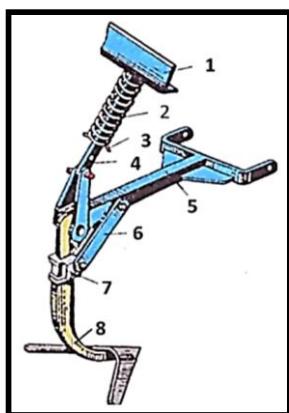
Рабочая секция культиватора КПС-4 с коротким грядилем: 1 – поперечный брус; 2 – пружина; 3 – чека; 4 – штанга нажимная; 5 – грядиль короткий; 6 – планка; 7 – державка; 8 – рабочий орган.
